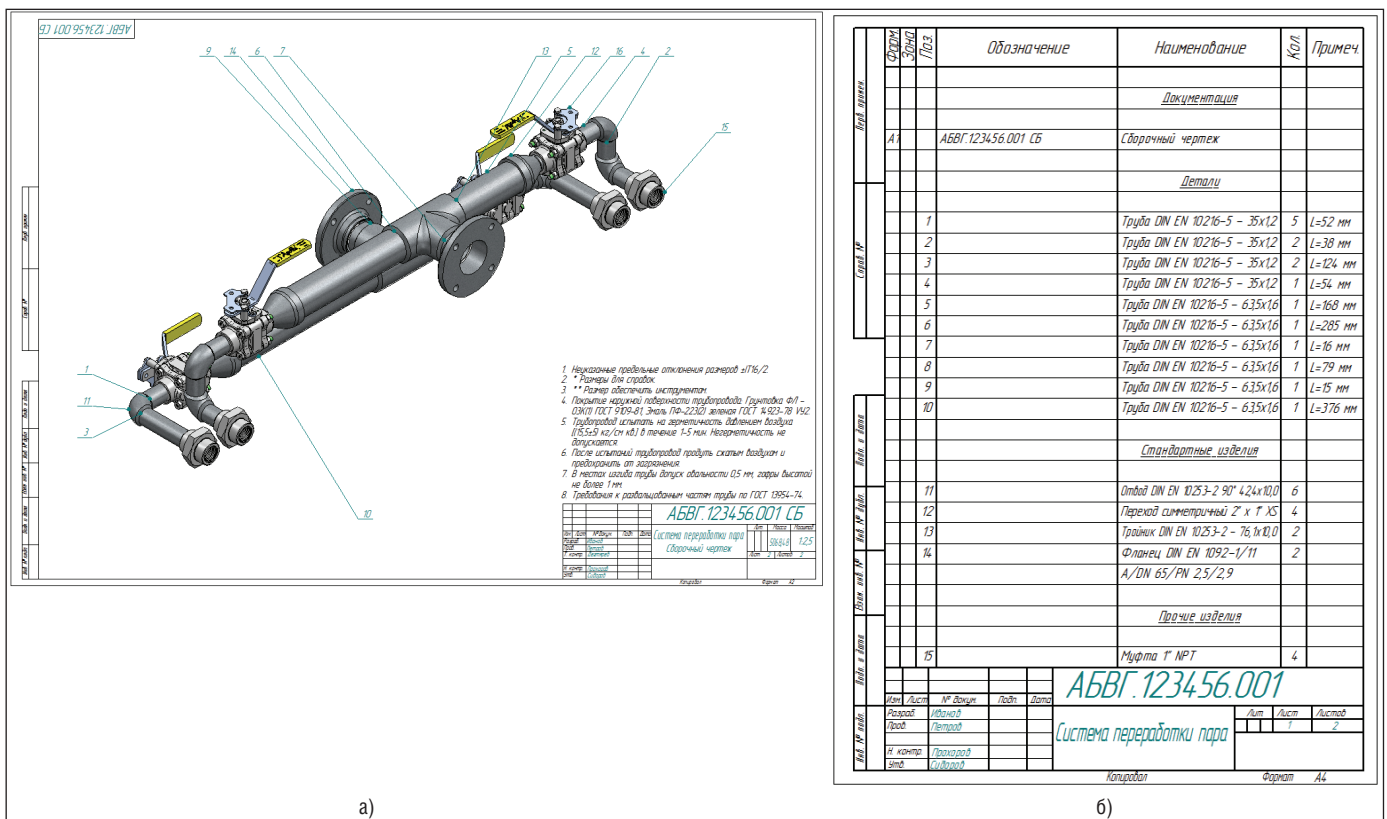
а – сборочный чертеж трубопровода, б – спецификация
